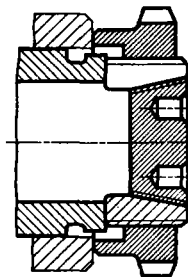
Стопорение кольцевой гайки пробкой с конической резьбой
